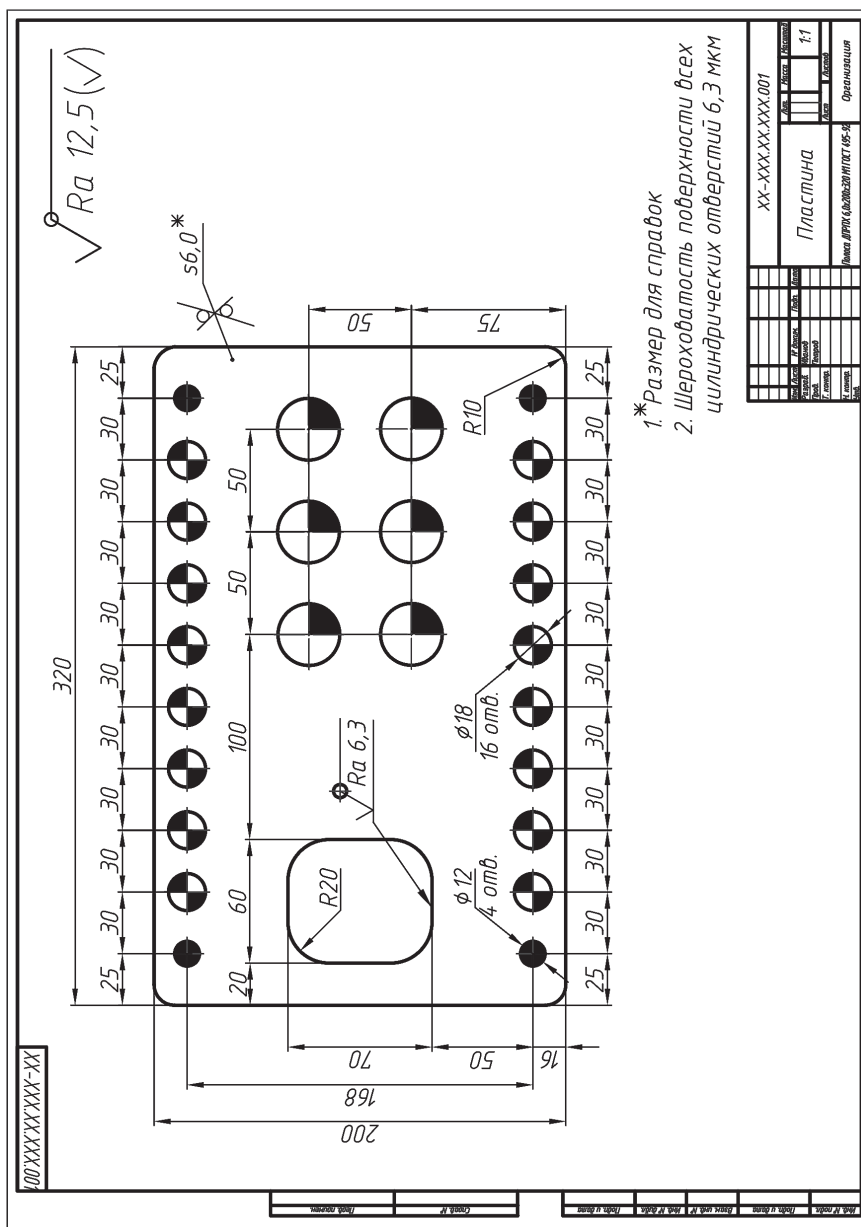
Чертеж детали «Пластина» после заливки отверстий
